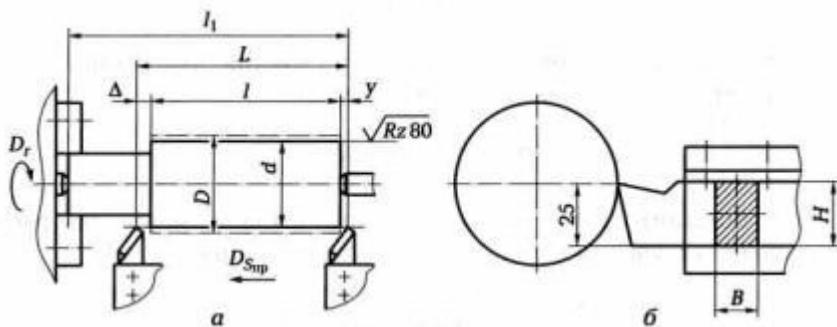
Эскиз обработки заготовки (а) и схема установки резца (б)
